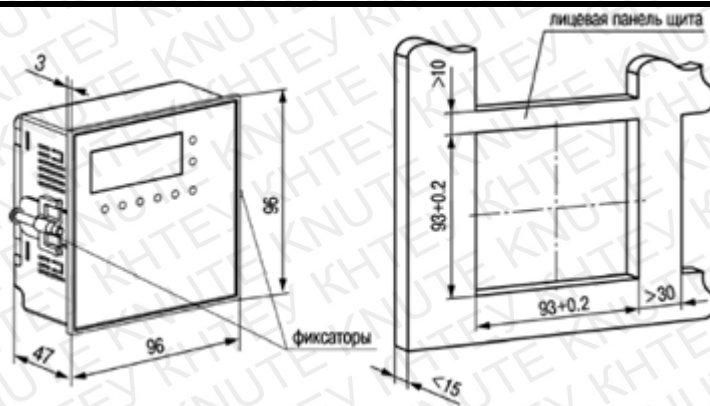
Габаритний рисунок вимірювального приладу
